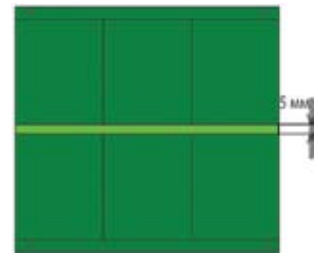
Свободное поле для центральной поддержки заготовок в печи оплавления
